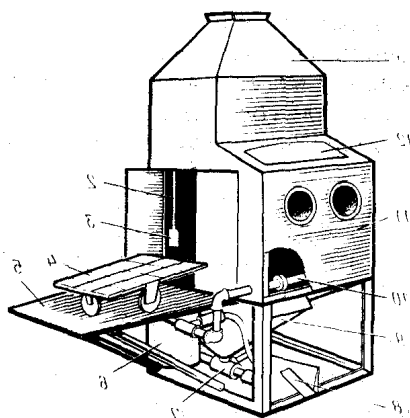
Установка для очистки деталей косточковой крошкой
